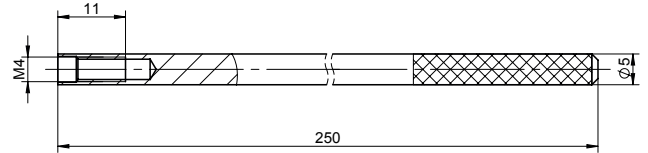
Ausziehwerkzeug für Blindsensor Typ 1319
